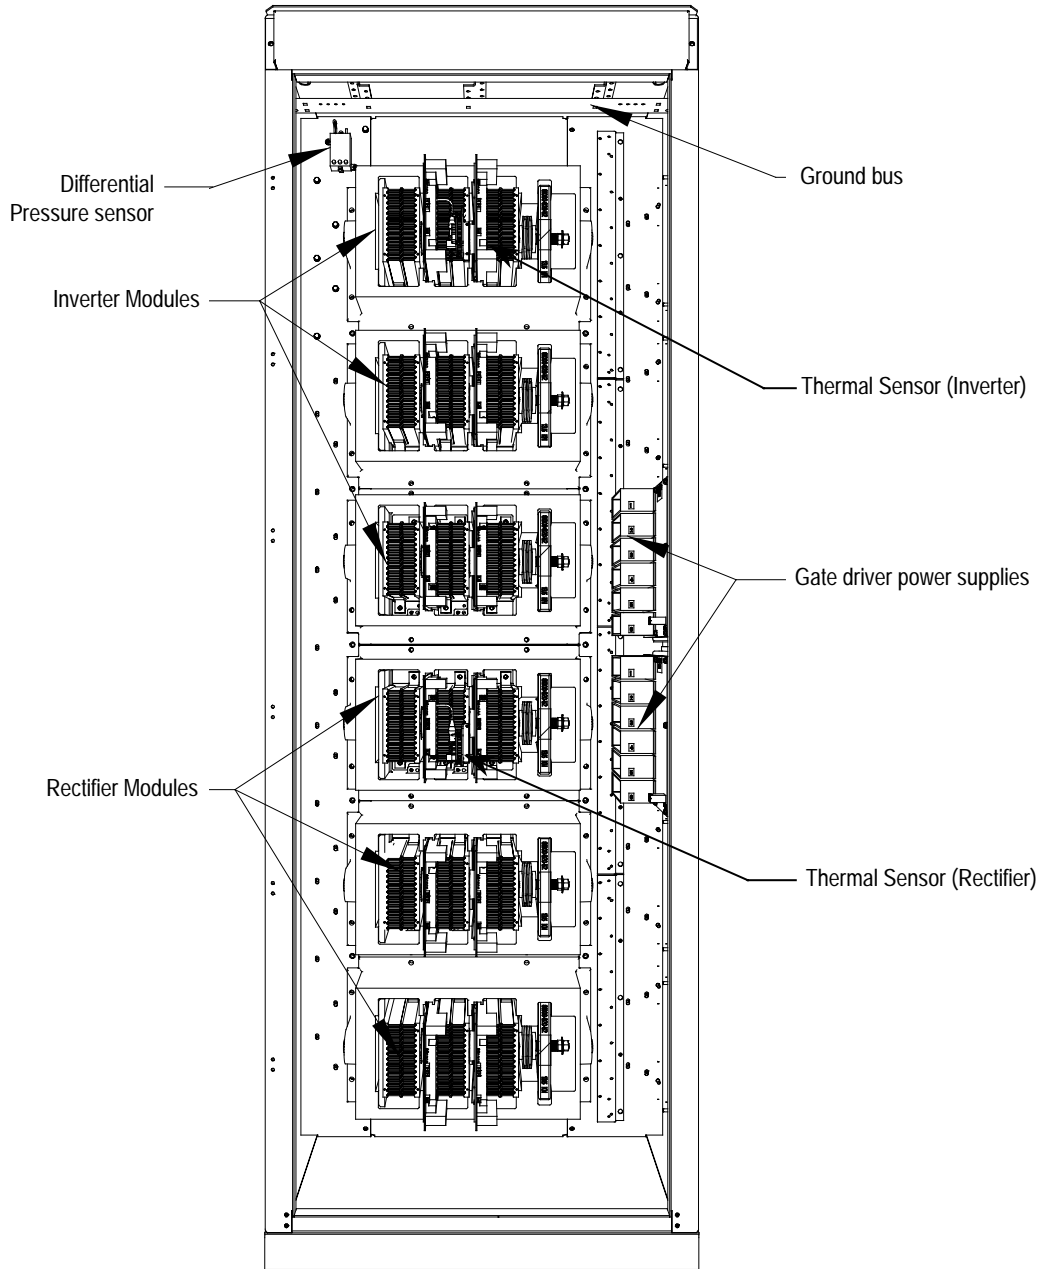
Baugruppen des Umrichterschaltchranks
